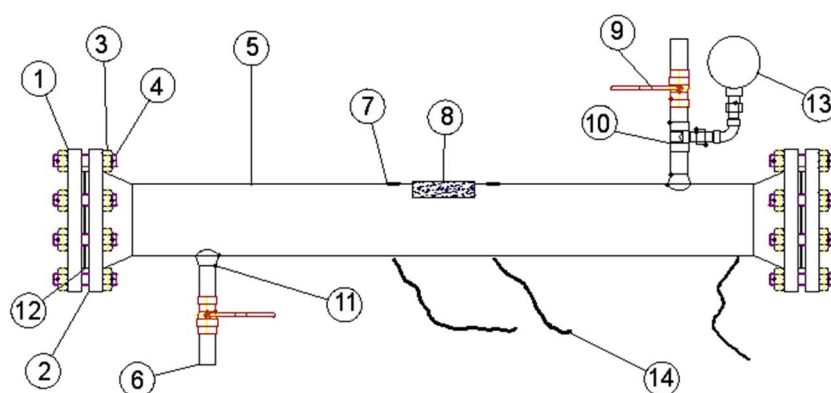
Desenho da Tubulação Ensaçada [Autor, 2022].
